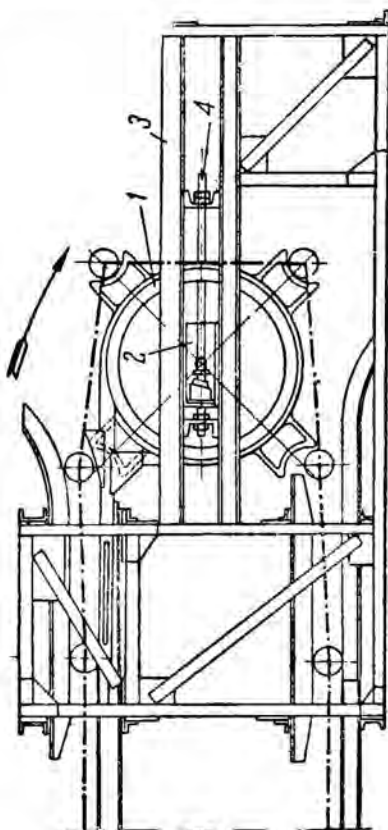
Винтовое натяжное приспособление с неподвижным шпинделем.
